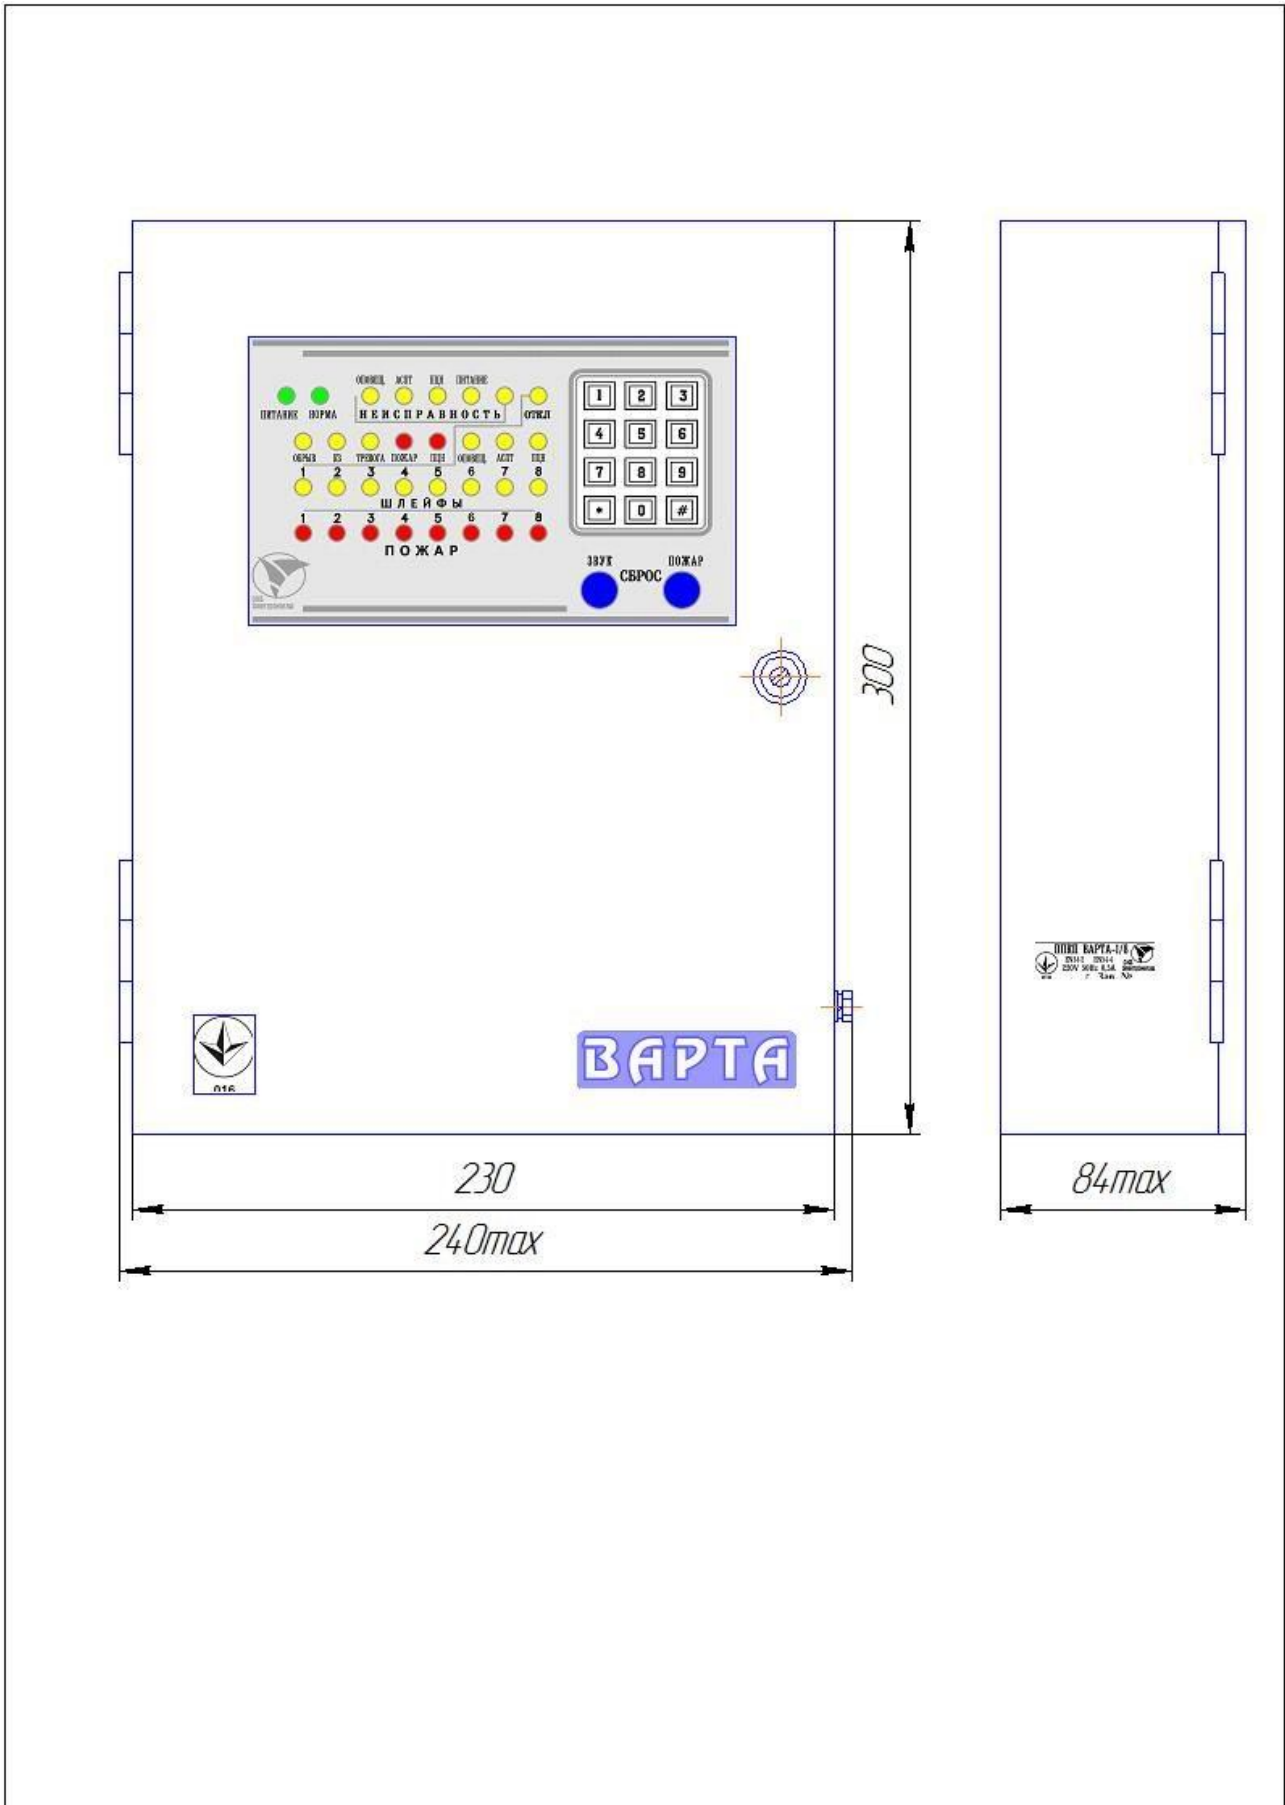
Внешний вид и габаритные размеры прибора «Варта-1/8»
